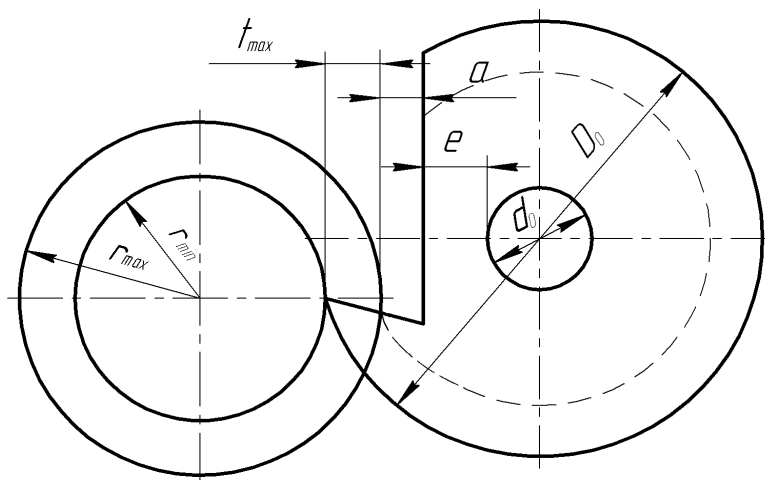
Схема определения наружного диаметра D_0 круглого фасонного резца
